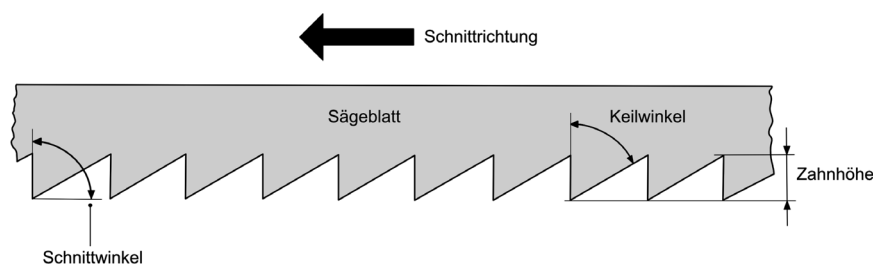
Zahn- und Winkelbezeichnung am Sägeblatt
